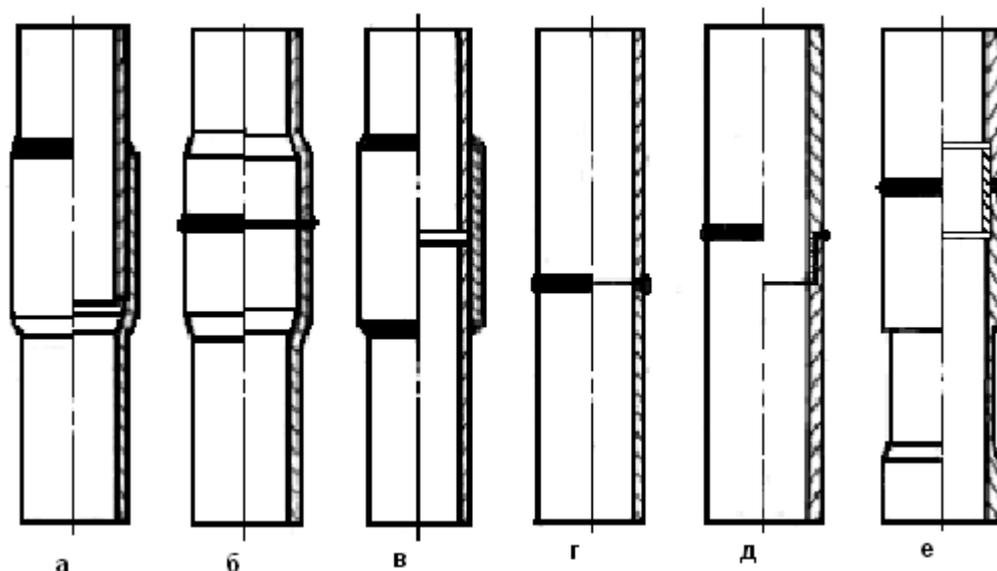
Конструкции сварных соединений обсадных труб
